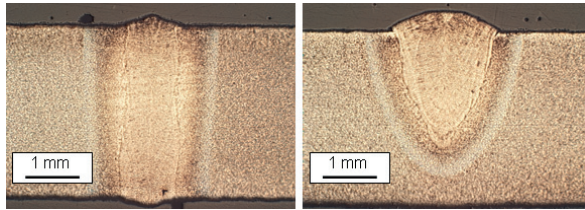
Querschliffe von Schweißnähten in Stahl mit (links) und ohne (rechts) Absaugung des Prozessrauchs.
